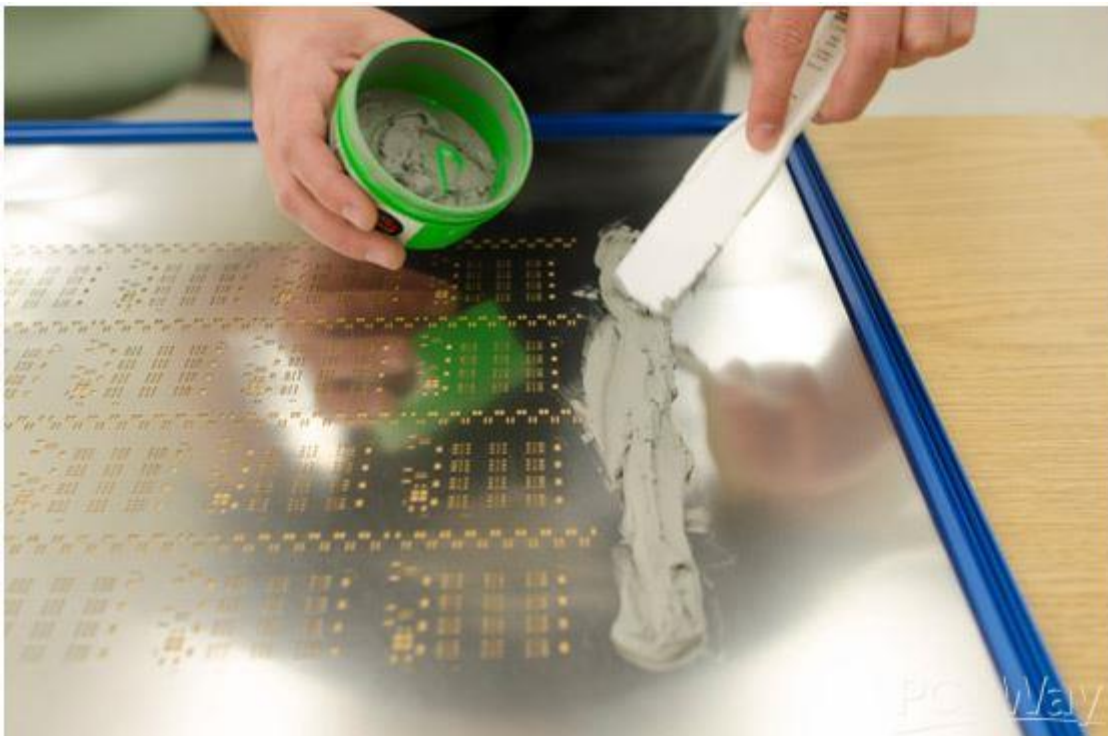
Representación del proceso de estañado para un panel PCB con un stencil con marco. Imagen de PCBWay.com
